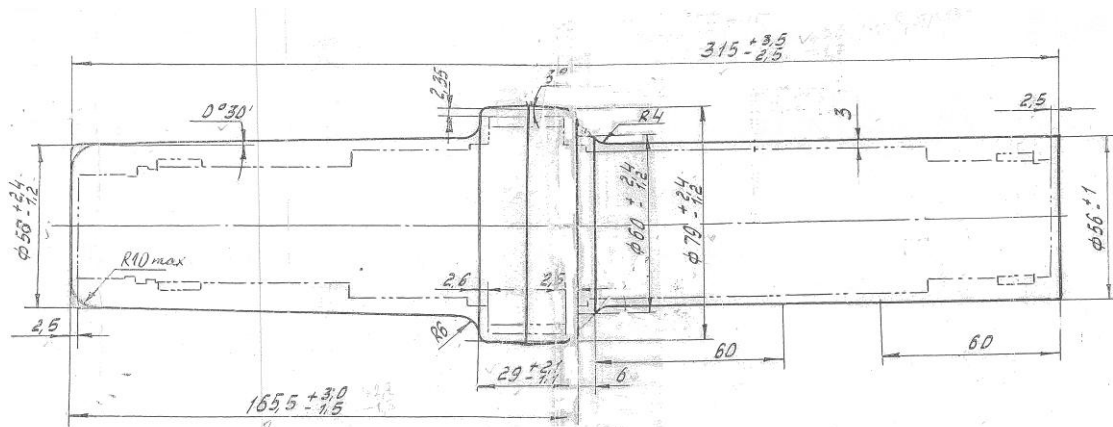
Чертёж поковки штампованной на горизонтально-ковочной машине
